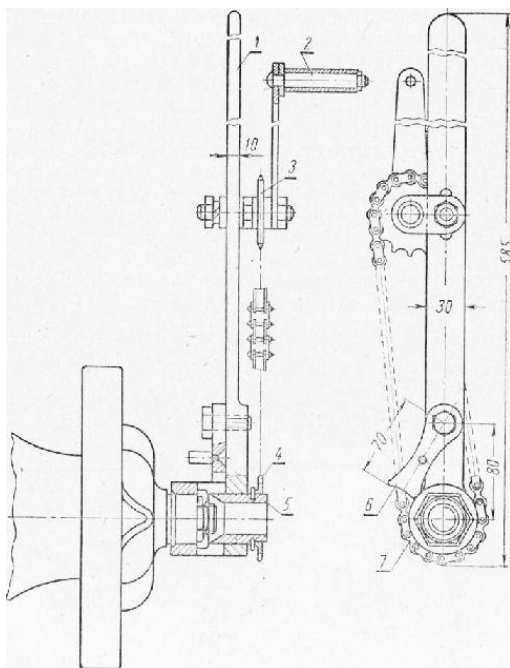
Ключ с цепным ускорителем: 1 — рычаг; 2 — рукоятка; 3 — ведущая звездочка; 4 — ведомая звездочка; 5 — головка ключа; 6 — собачка; 7 — цепь
